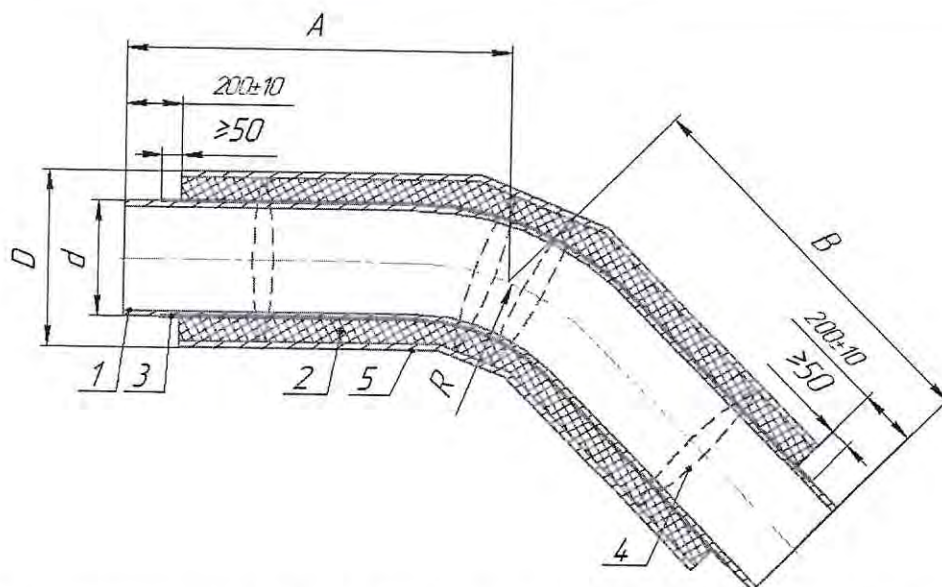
Конструкция крутоизогнутого отвода с теплоизоляционным покрытием
